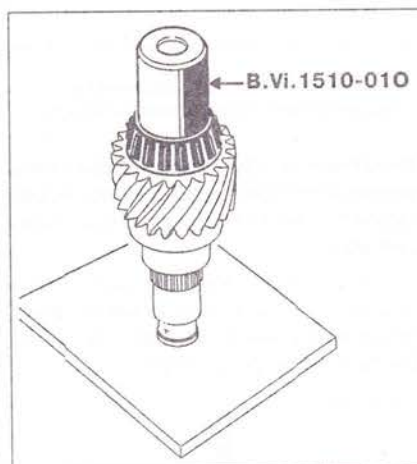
б. Установка подшипников на коротком вторичном вале.
